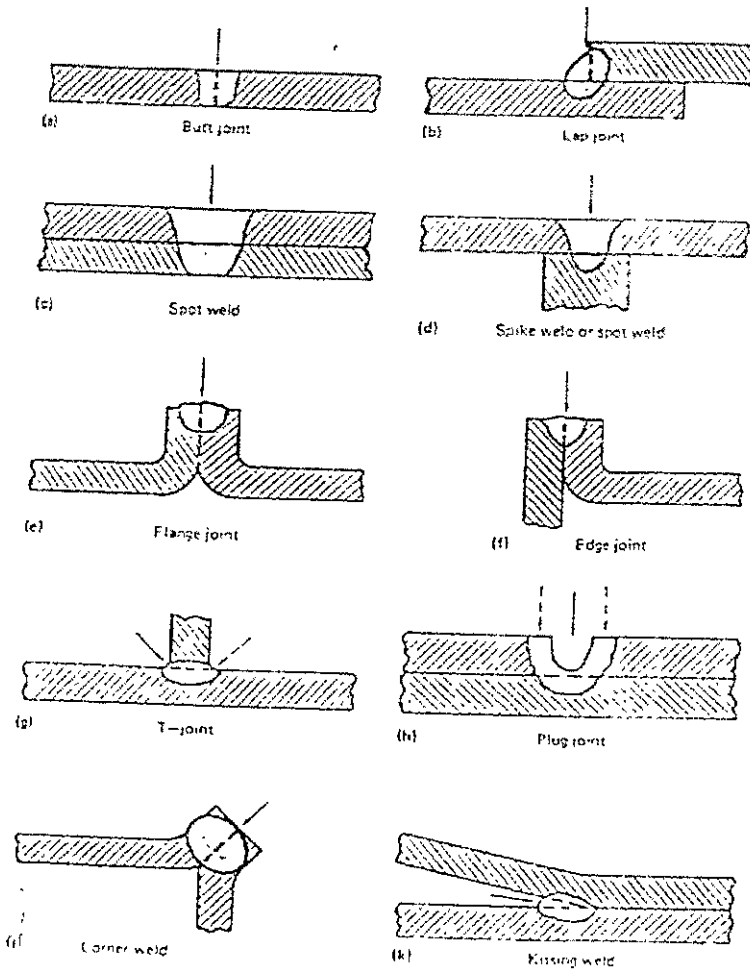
Diseño de juntas para soldadura con haz de láser en hojas de metal: Las flechas muestran la dirección del haz de láser
